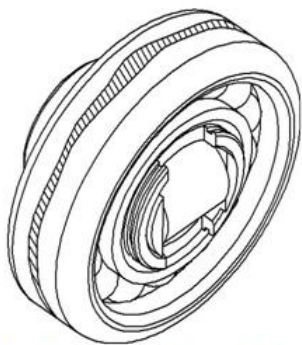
Схема кольцевых трещин на подшипнике.
